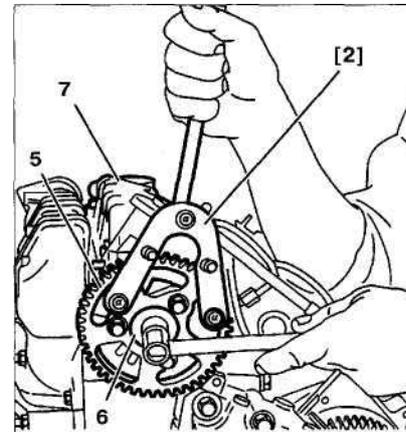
Снимите ступицу 6 с помощью приспособления [2]. Снимите шкив 5 распределительного вала и верхнюю часть крышки 7 головки блока цилиндров.
